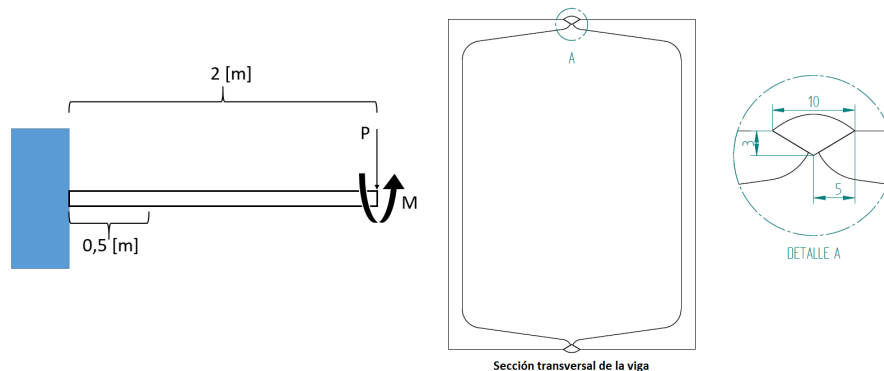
Sección de la viga y aplicación de la fuerza y momento. En el detalle A las cotas están en mm
